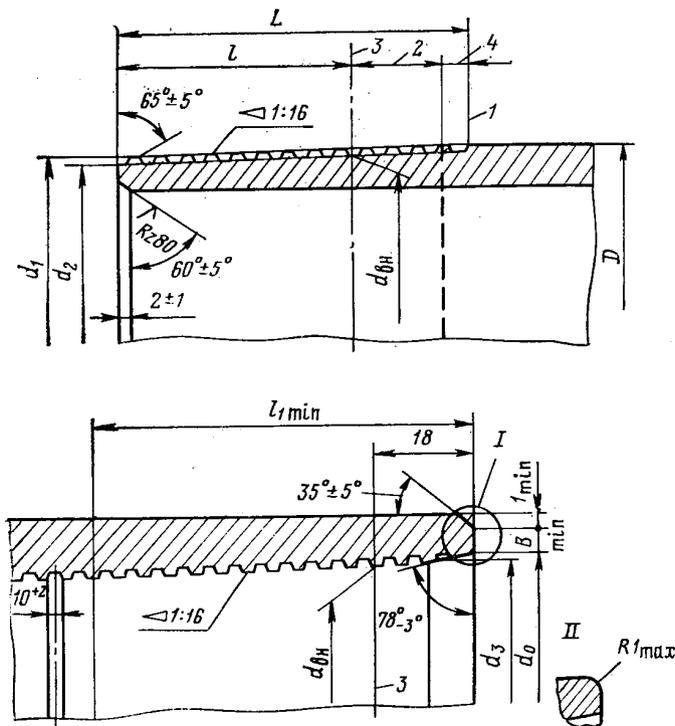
Размеры резьбовых соединений труб ОТТМ:
